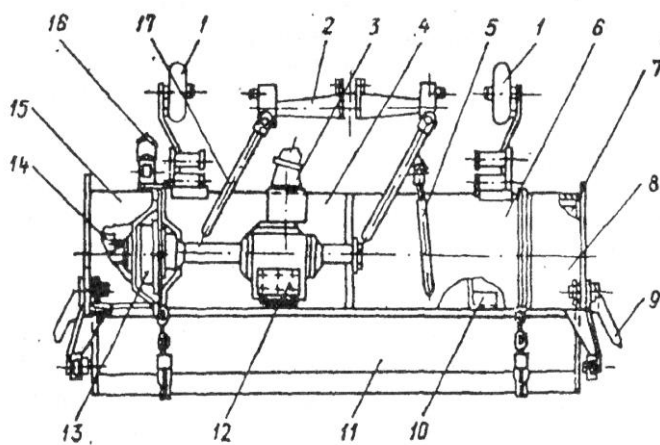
Фреза садова ФПШ-200: 1 – колеса опорні; 2 – начинка; 3 – карданний вал; 4 – кожух; 5 – штанга обмежувача; 6 – рама середня; 7 – фрезерний барабан правий; 8 – рама права; 9 – лапа стрілоподібна; 10 – фрезерний барабан середній; 11 – кришка рухома; 12 – редуктор конічний; 13 – редуктор циліндричний; 14 – фрезерний барабан лівий; 15 – рама ліва; 16 – рама розпушувача; 17 – несуче обладнання.
